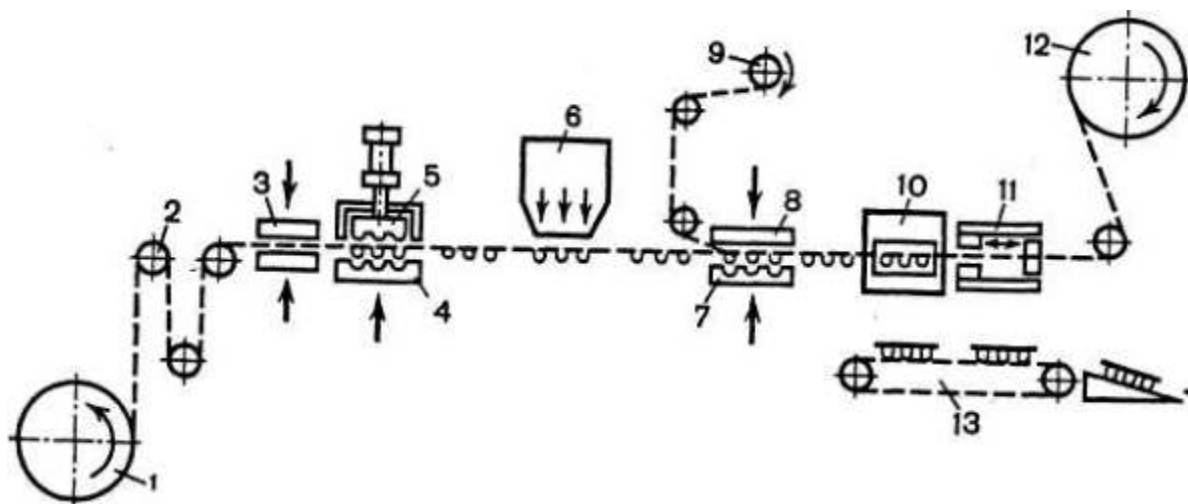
Схема автомату періодичного формування блістерів. 1- ролон з плівкою; 2- петлеутворювальний пристрій; 3- вузол нагріву; 4,5- нижня та верхня матриці (вузол формування); 6- бункер; 7,8- нижня та верхня плита (вузол зварювання); 9- ролон з фольгою; 10- вузол виробки; 11- протягувальний пристрій; 12- ролон відходів або залишків; 13- конвеєр.
